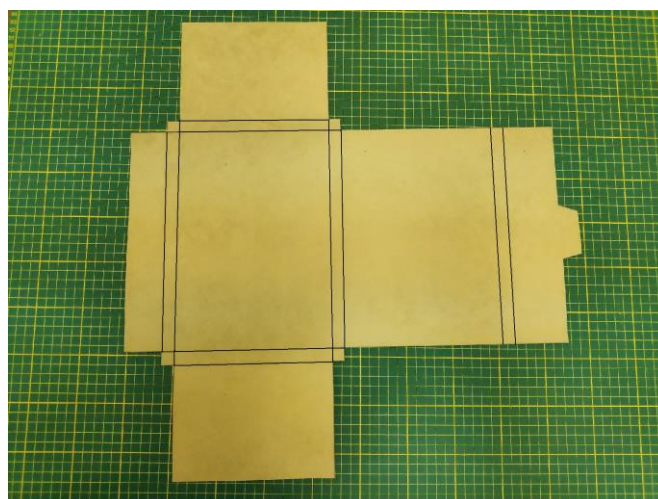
Готовая заготовка контейнера с вдавленными линиями сгиба
